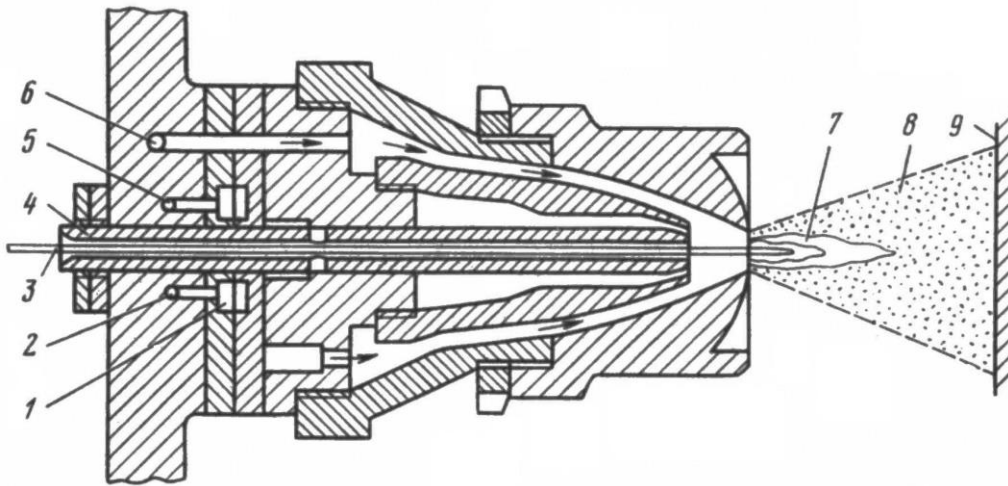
Розпилювальна головка газоплазмового апарату:
